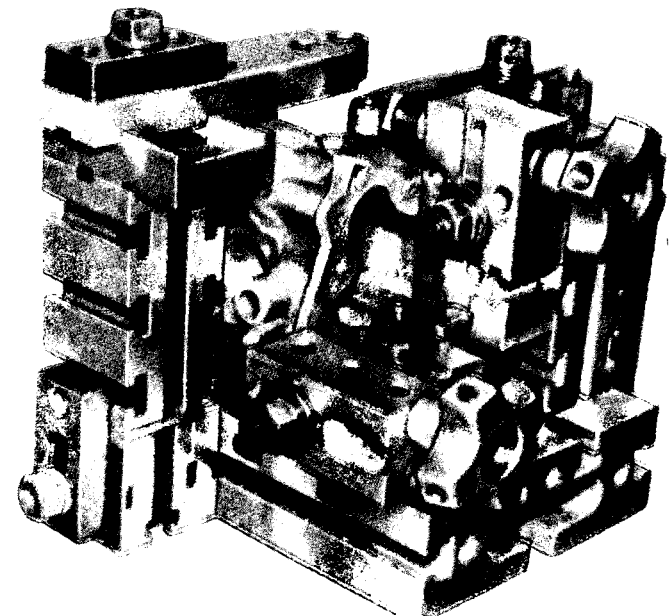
Приспособление для сверления двух отверстий в корпусе
